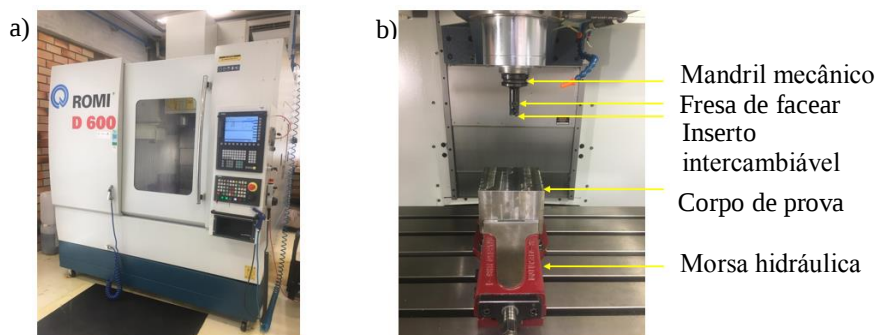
Equipamentos utilizados: a) Centro de usinagem ROMI® D600 e b) Conjunto montado
